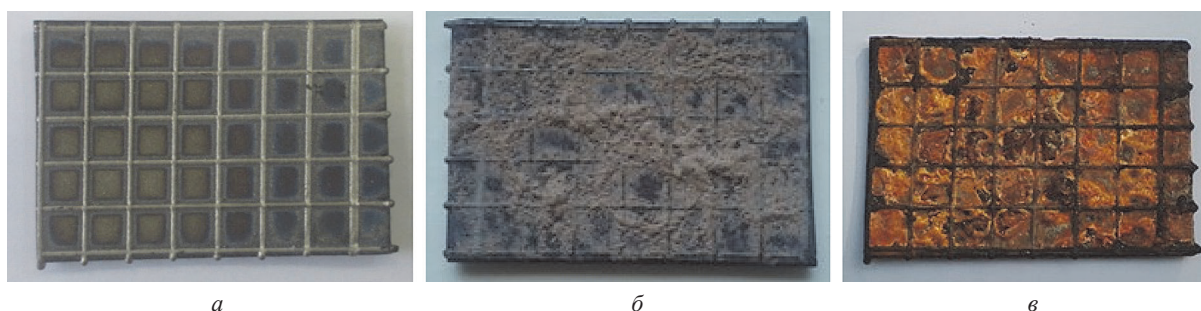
Этапы создания композиционного покрытия: *а* – стальной образец с нанесенной сеткой; *б* – образец, покрытый флюсом; *в* – образец после индукционной наплавки перед механической обработкой
